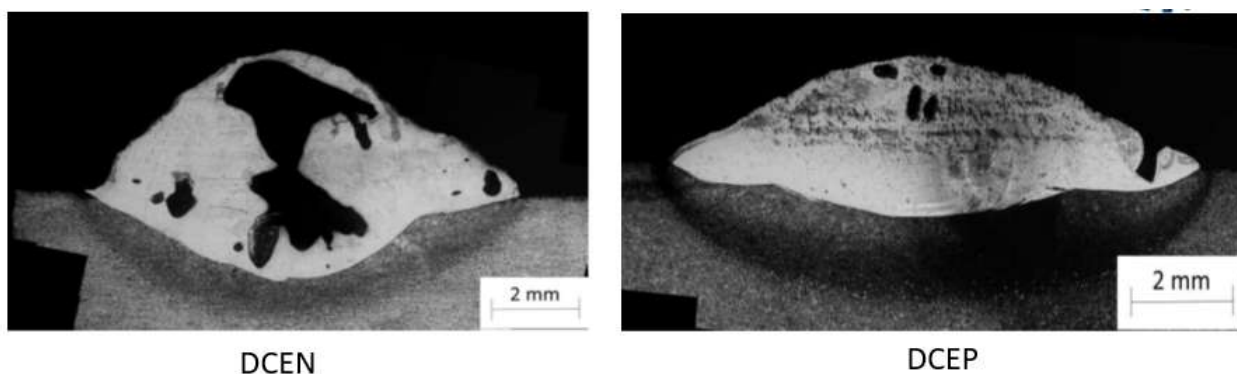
Cordões de solda produzidos a 30m de profundidade, 180A, DCEP, E312
